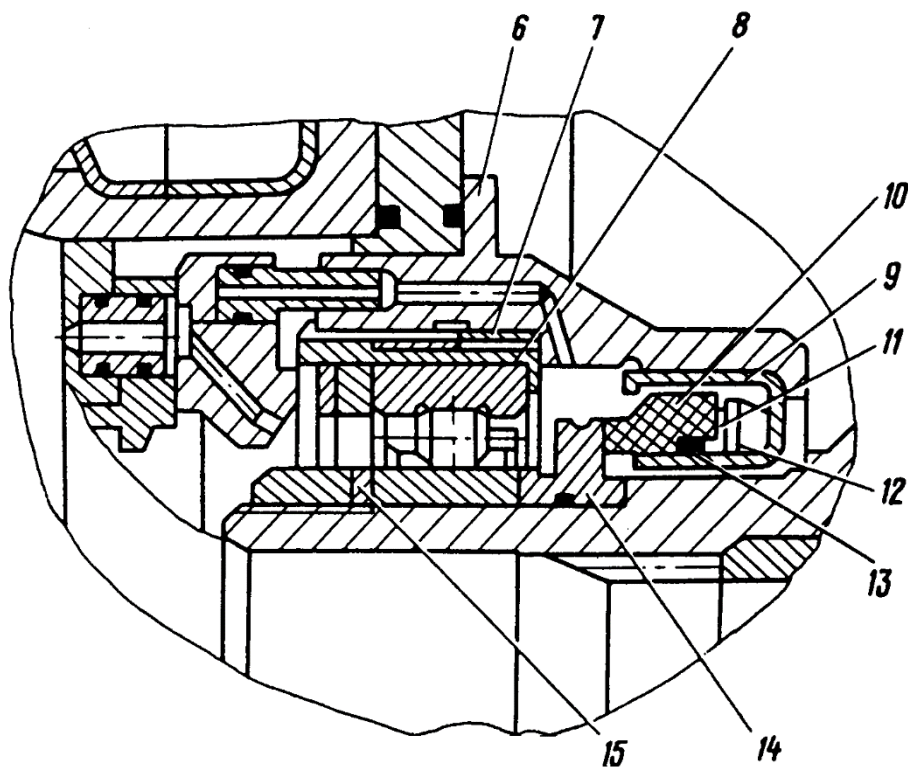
Podélný řez rotorem kompresoru [13]
